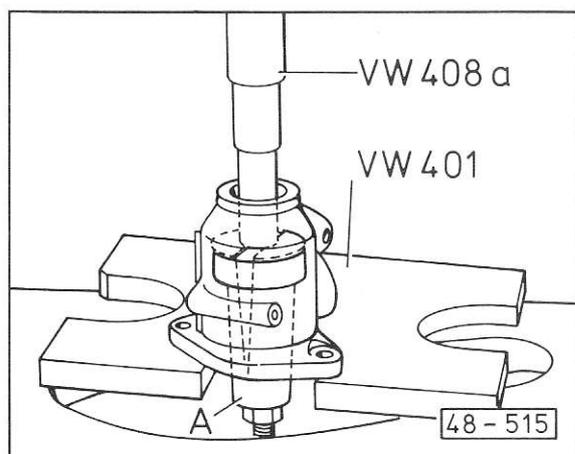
Roulement à aiguilles: l’enlever du boîtier de soupape
